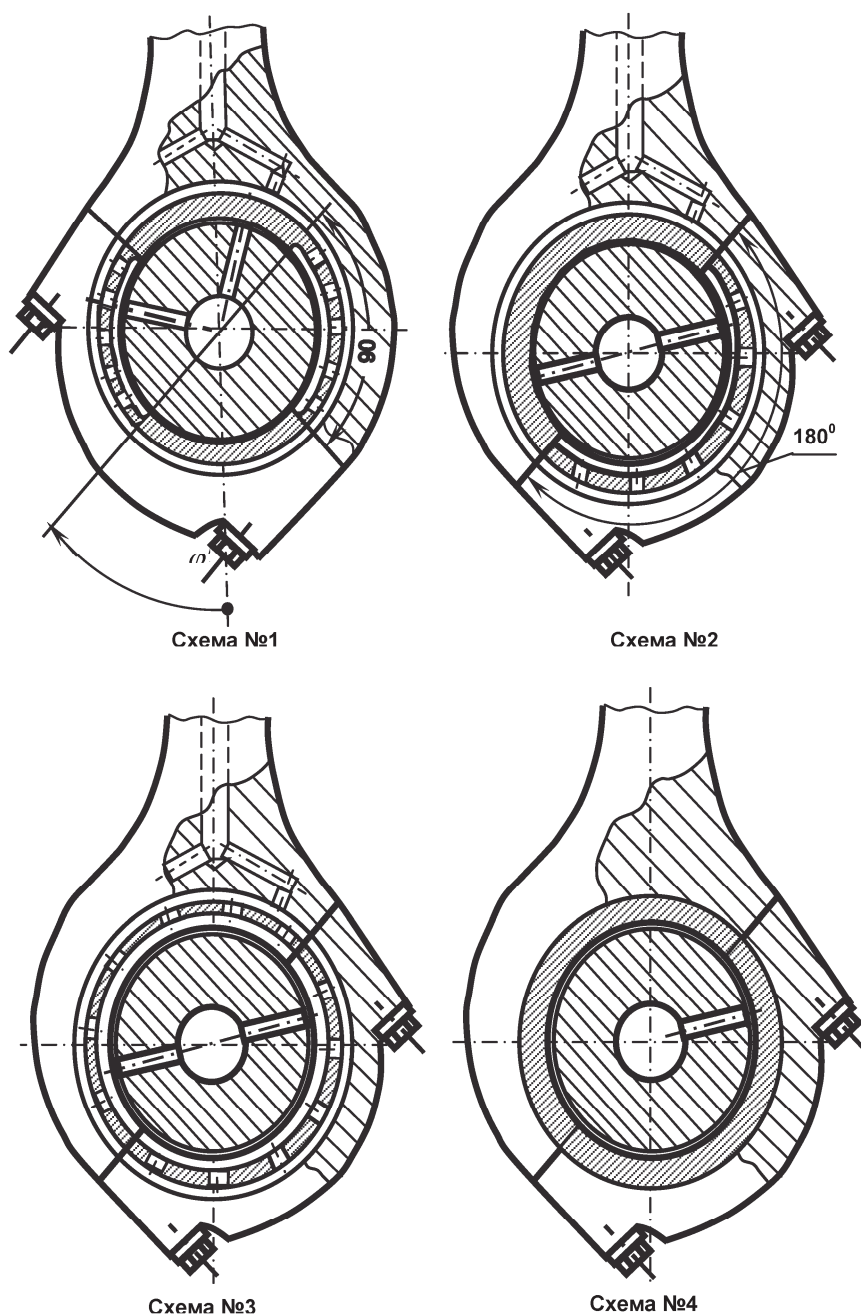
Возможные схемы подачи смазки в шатунный подшипник двигателя ДМ-21
